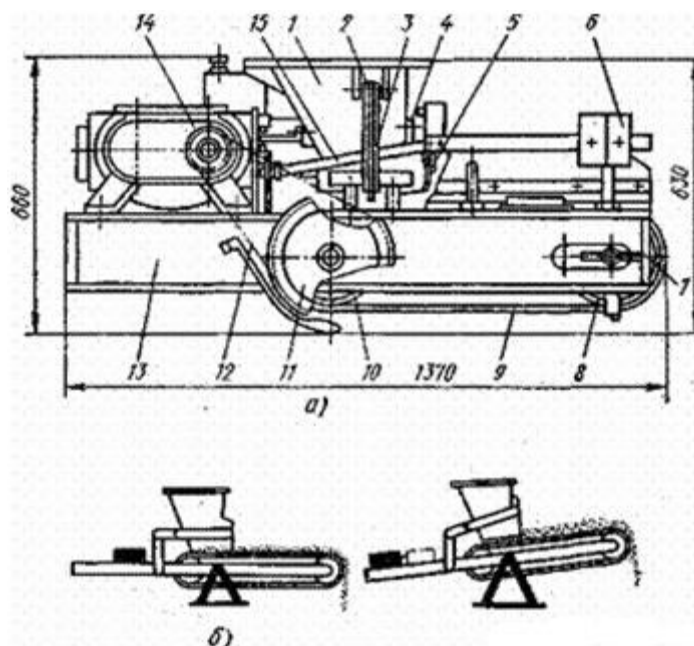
Весовой дозатор непрерывного действия СБ-71А
